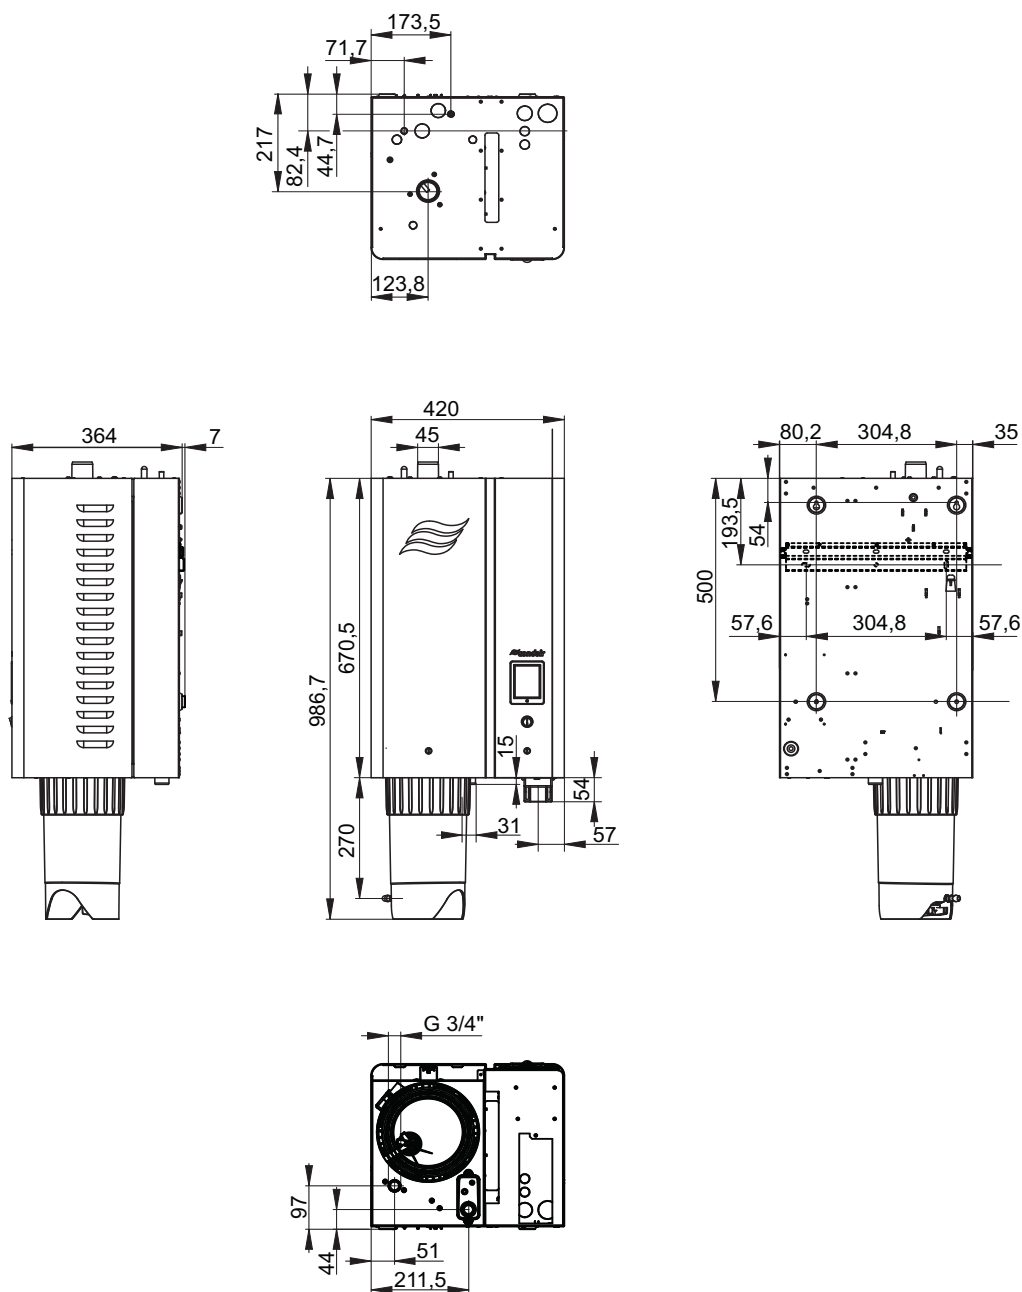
Габаритный чертеж корпуса малого типоразмера (размеры в мм)
